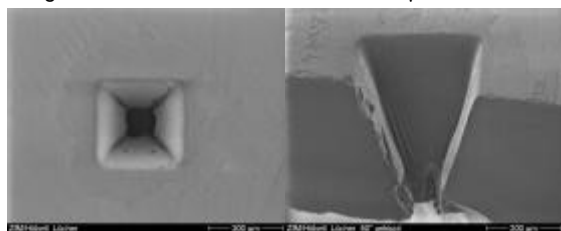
REM-Aufnahmen ; Drauf- und Seitenansicht einer mittels CO₂-TEA-Laserpulsabtrag in Pyrexglas (d=500 µm) eingebrachten Öffnung.
